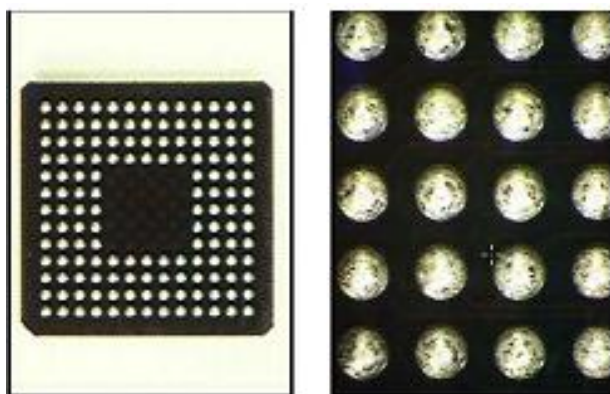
BGA pouzdro s kulovými vývody (Solder Balls) spojenými s vlastním čipem drátovými vývody. [3]
